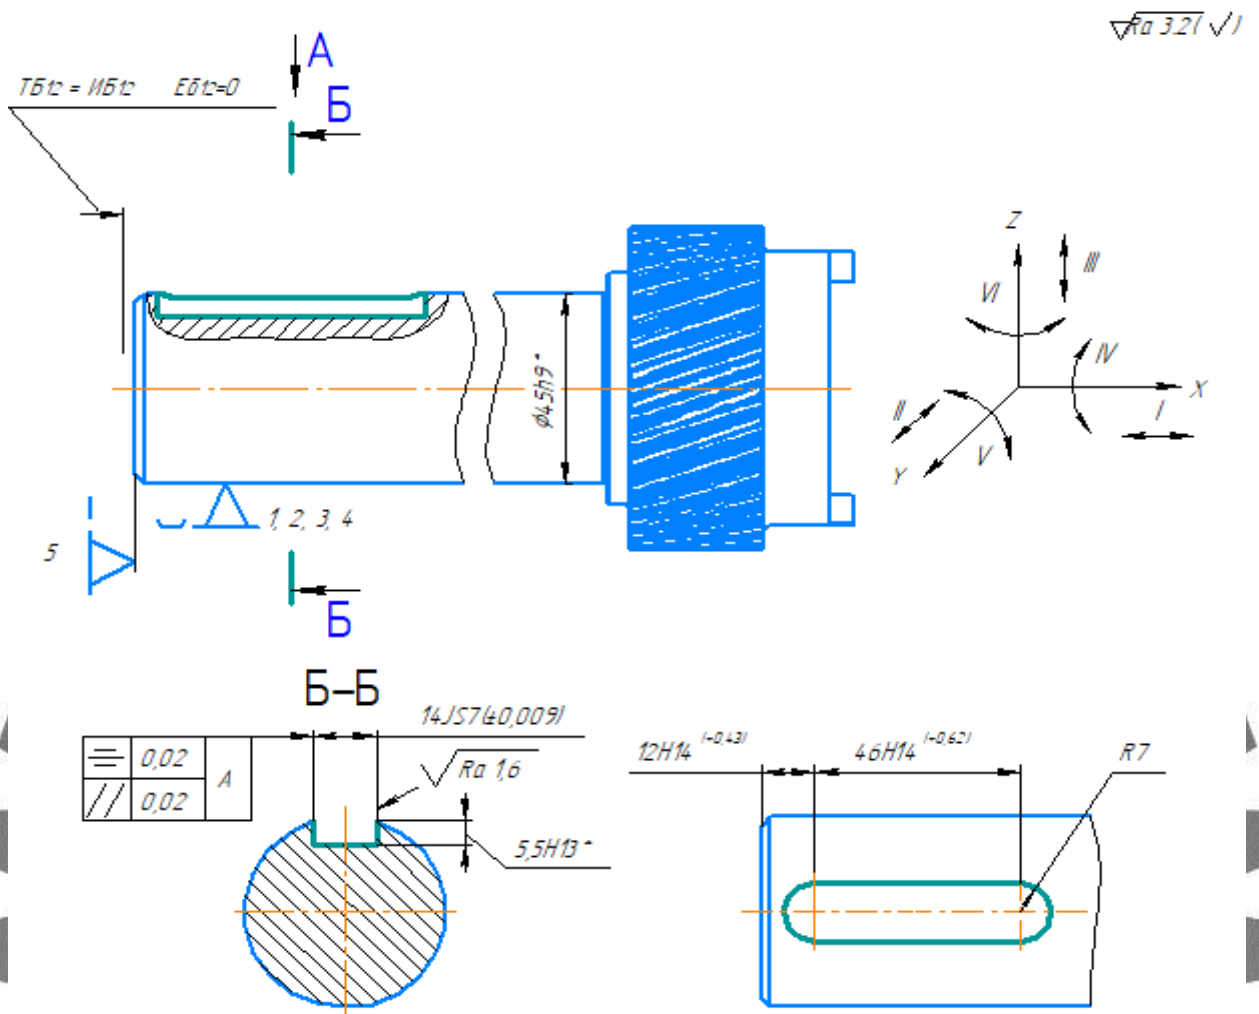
Схема базування заготовки для обробки шпонкового пазу
